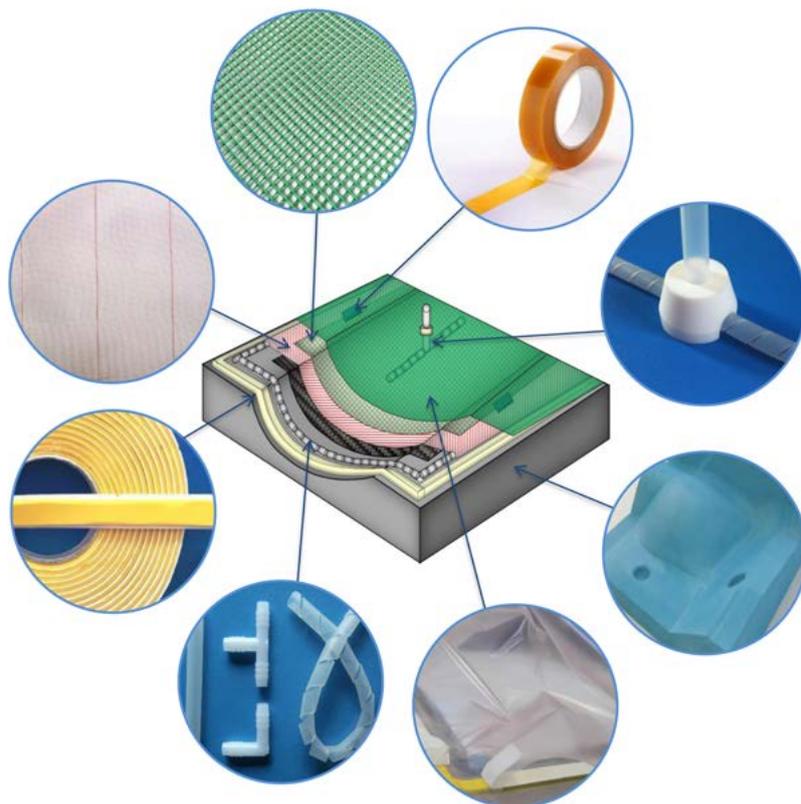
Стандартная схема сборки мешка в процессе вакуумной инфузии.
